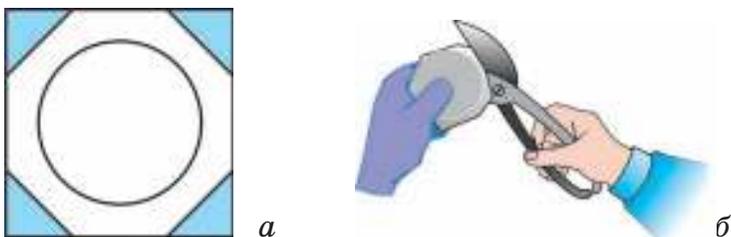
Резка тонколистового металла ножницами по криволинейному контуру:
